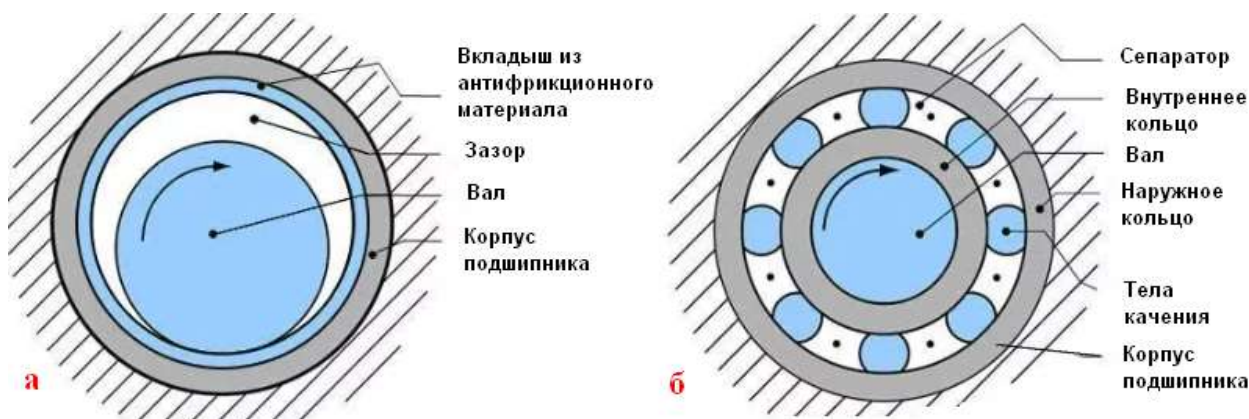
Устройство подшипников: а – скольжения, б - качения
